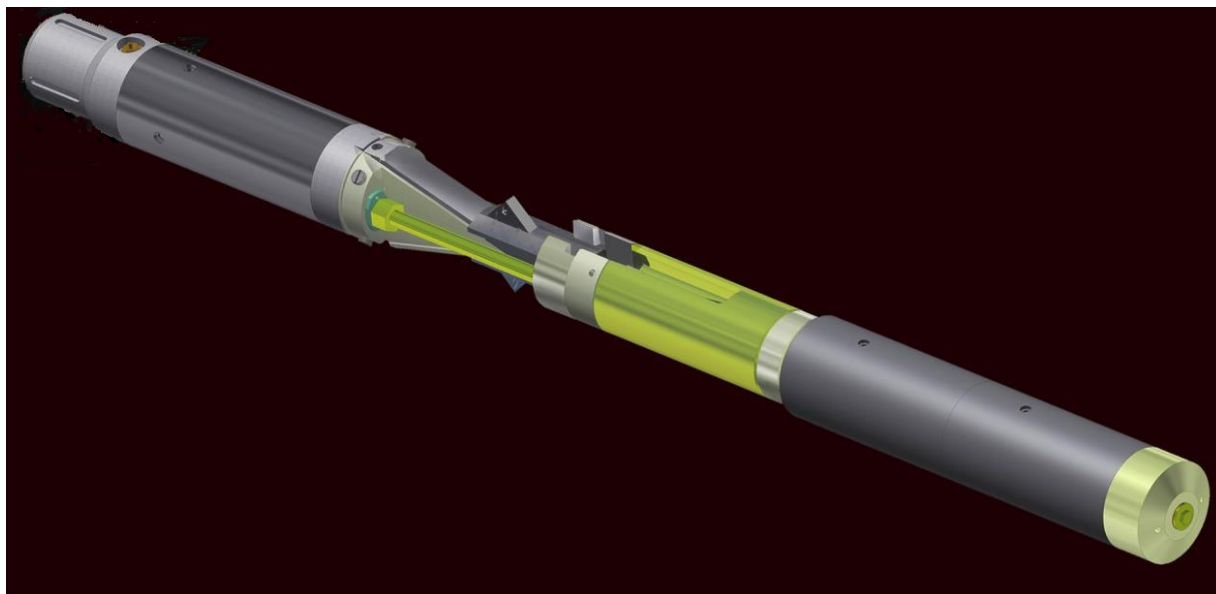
Внешний вид гидромеханического прокалывающего перфоратора ПГМП-114
